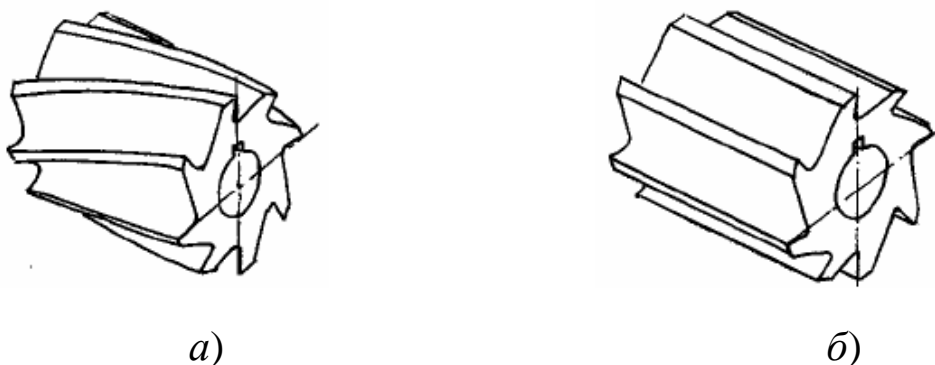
Разновидности наклона зубьев цилиндрической фрезы: с винтовым зубом (а) и с прямым зубом (б)
